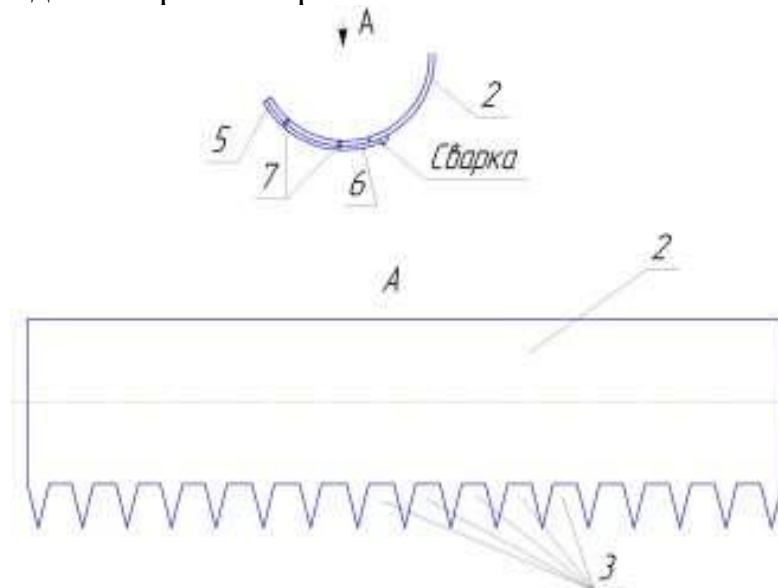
Корпус: 2 – корпус; 3 – вирізи; 4 – накладки з фторопласту; 5 – протиріжучі пластини; 6 – пальці; 7 – гвинти
